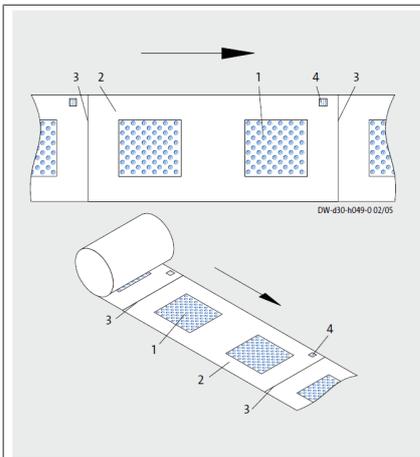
Immagine di stampa - Uso di una tacca di stampa separata
